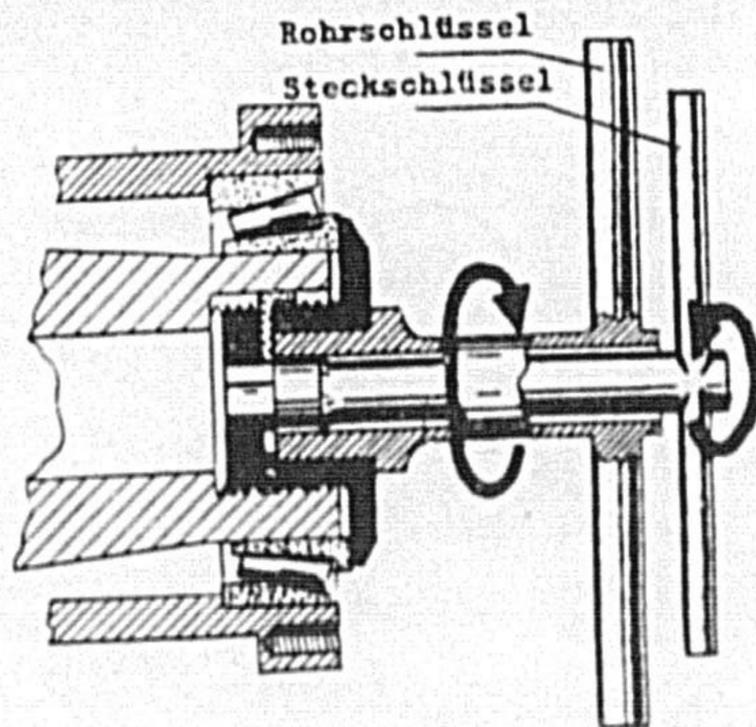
Festschrauben der Haltemutter und Gegenmutter
